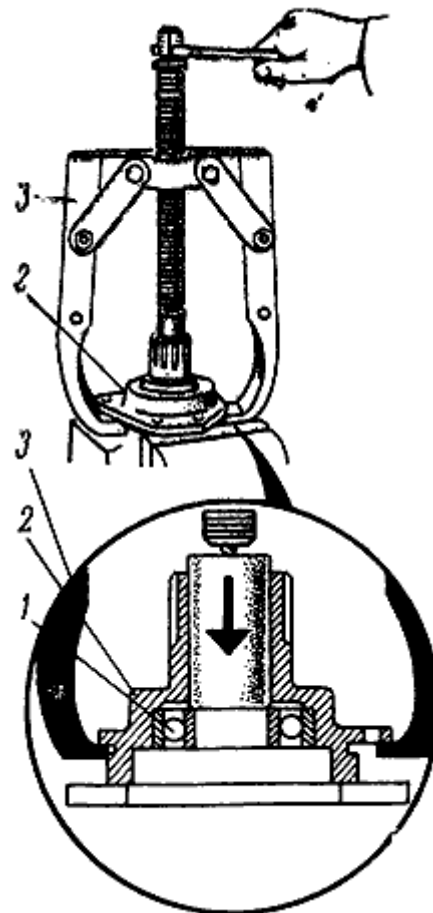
Выпрессовка подшипника ведущего вала привода ВОМ из кронштейна отводки:
